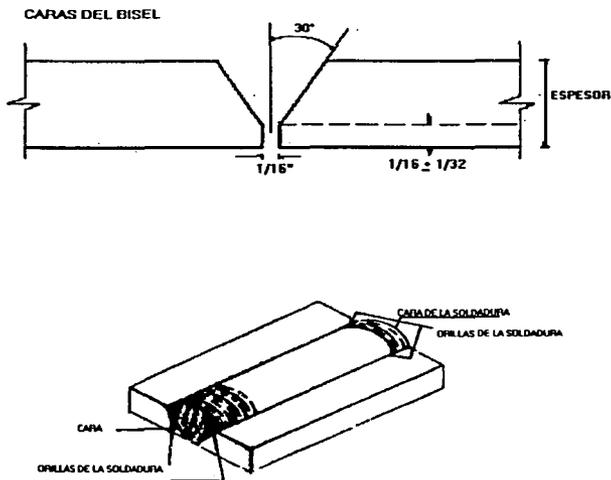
A) Bisel y B) Soldadura aplicada sobre un bisel Conformado con dos Caras de Tubo
